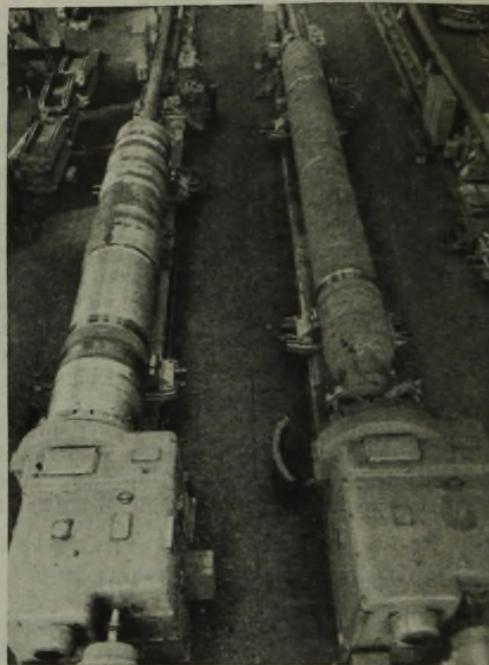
Nahtlos hohl geschmiedete Hochdruckmäntel in der Bearbeitung auf Großdrehbänken.
